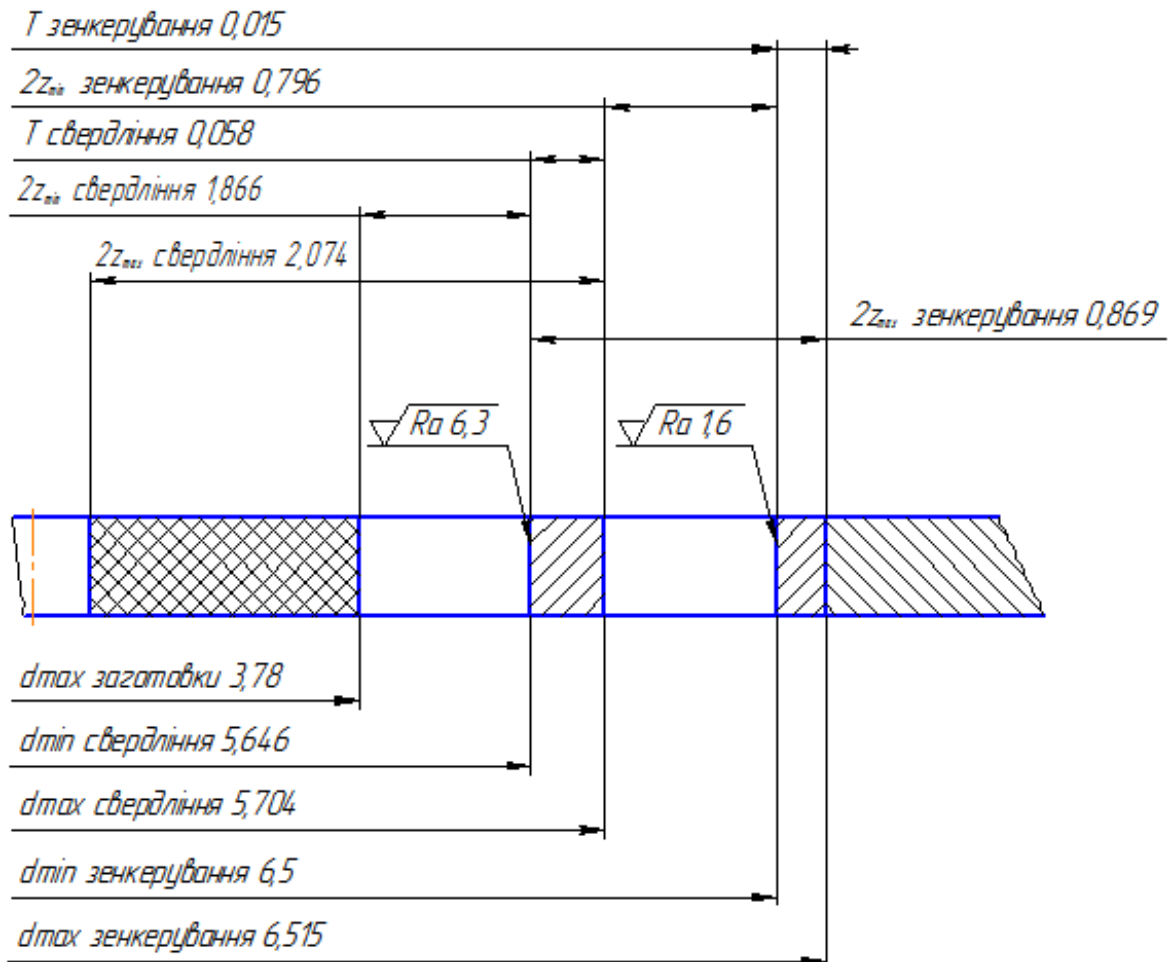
Схема розташування припусків та допусків
